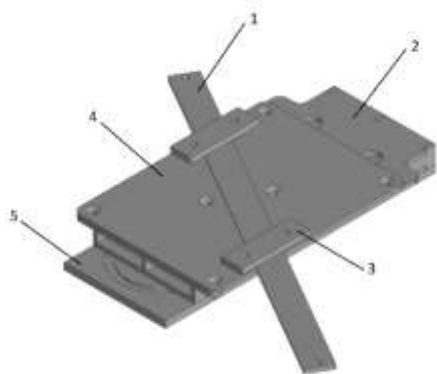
Общий вид сборки приспособления для фрезеровки пазов на стальных бандажах. 1 – стальной бандаж, 2- корпус сварной, 3 – прижим, 4 – упор задающий угол, 5 – поперечные салазки суппорта токарного станка.
